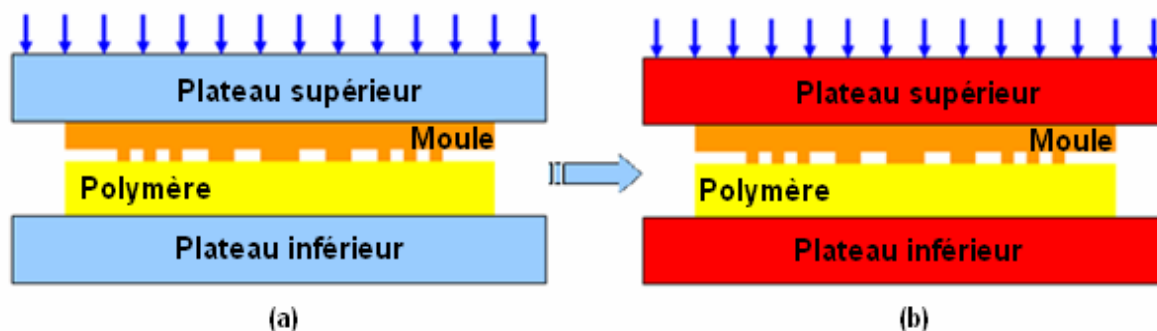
Schéma descriptif des deux sous étapes de mise en forme du procédé de réplcation par estampage à chaud (a) mise en contact des outillages et de la plaque (b) et chauffage de l'ensemble.
